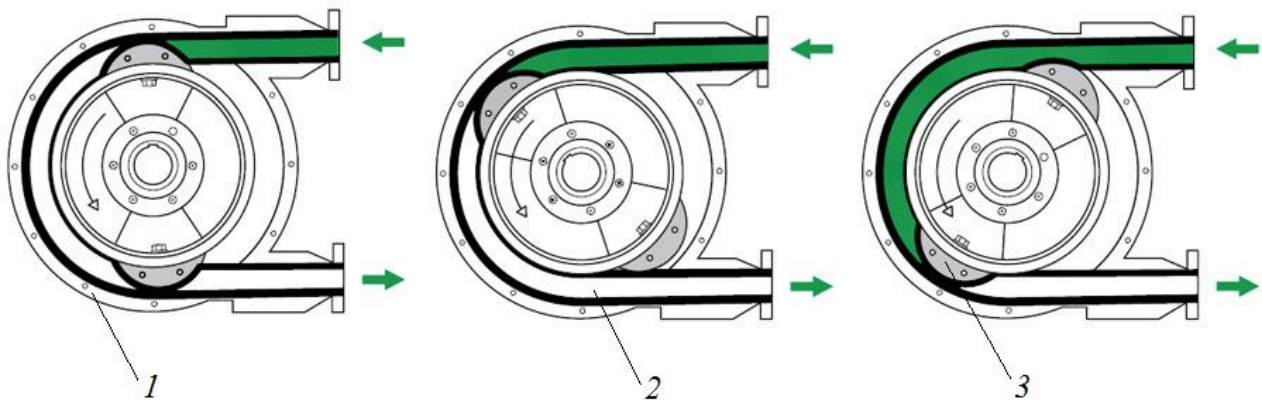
Схема принципу роботи перистальтичного насоса: 1 – корпус; 2 – гнучка трубка; 3 – ротор із робочими виступами [5].
